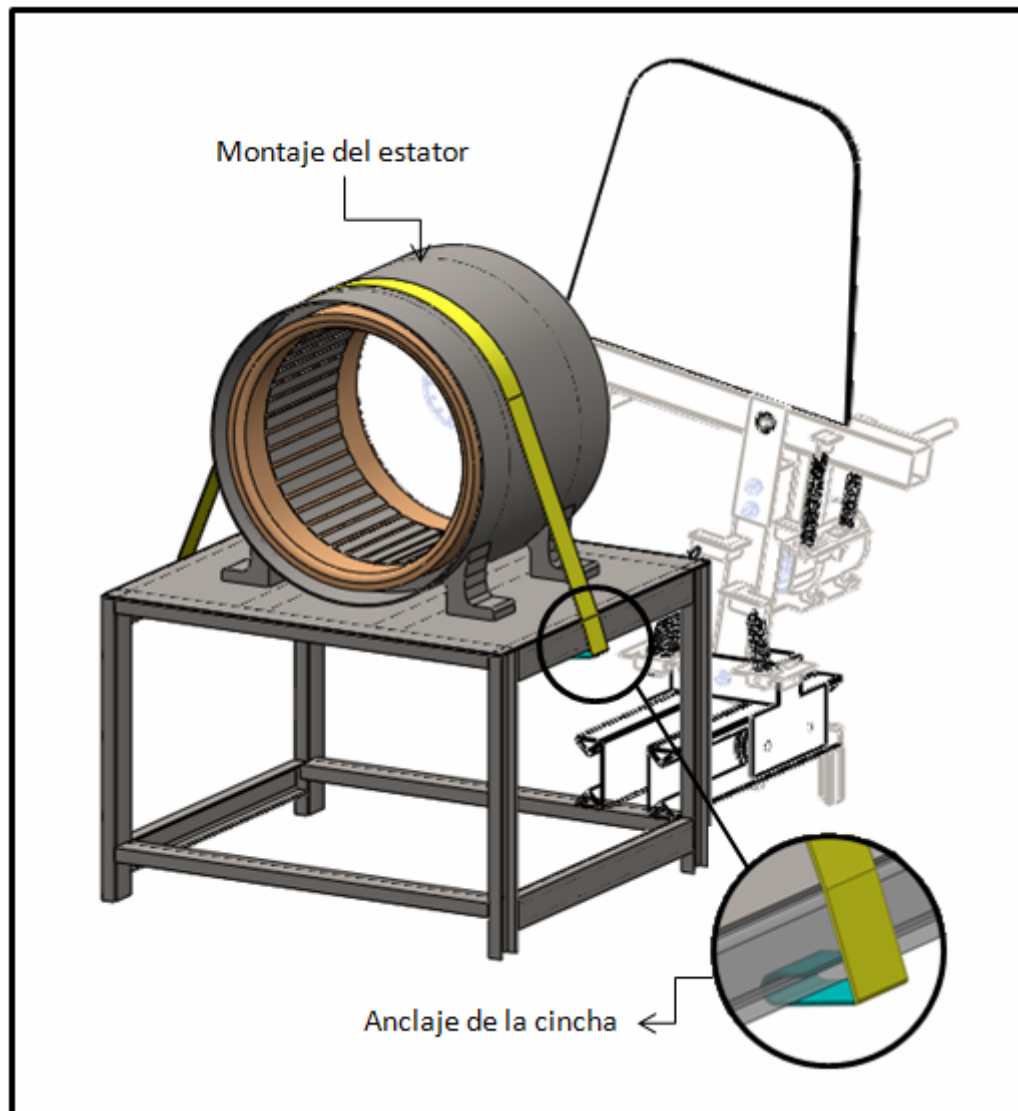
Montaje y anclaje del estator [Fuente propia].
